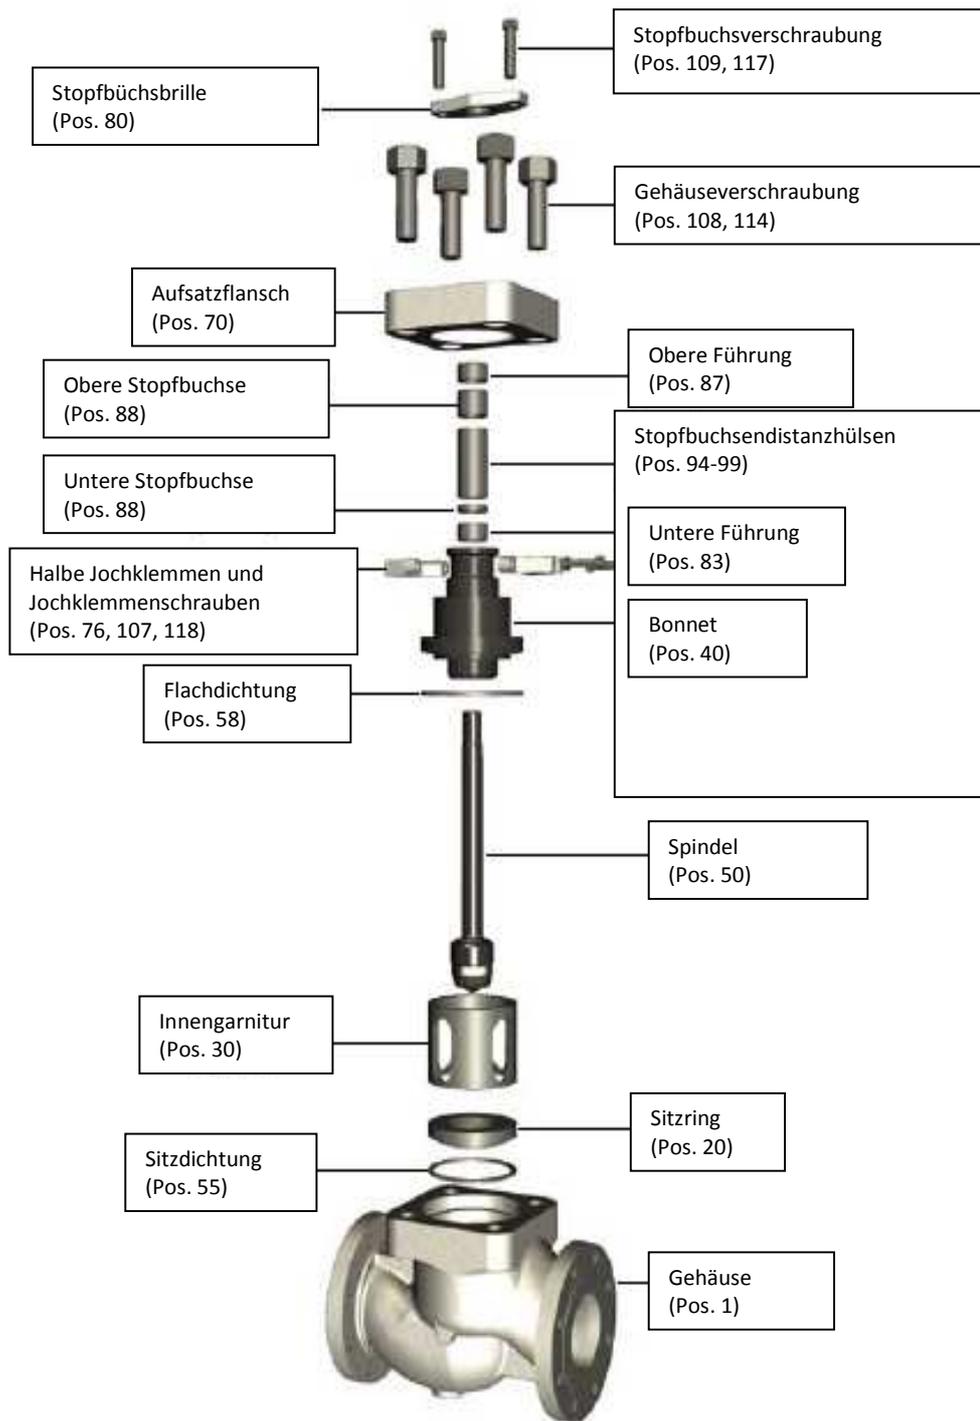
Explosionszeichnung Mark One - Gehäusebaugruppe
